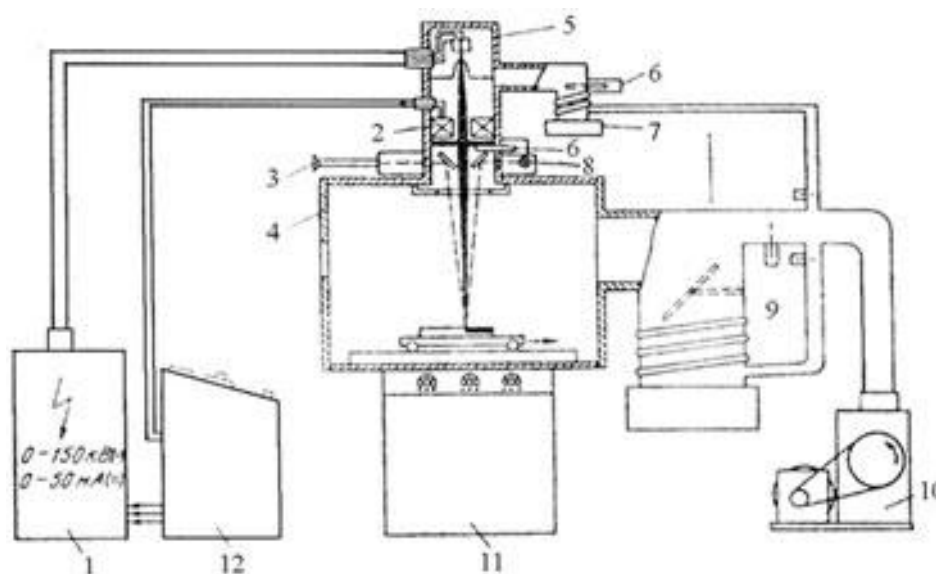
Принципиальная схема установки для электронно-лучевой сварки: 1 - высоковольтный источник питания; 2 - магнитное отклоняющее устройство; 3 - телескопическое устройство для наблюдения; 4 - сварочная камера; 5 - электронная пушка; 6 - вентиль; 7 - диффузионный насос; 8 - освещение; 9 - вакуумный вентиль; 10 - роторный форвакуумный насос; 11 - пульт управления движением детали; 12 - электрический пульт управления.
